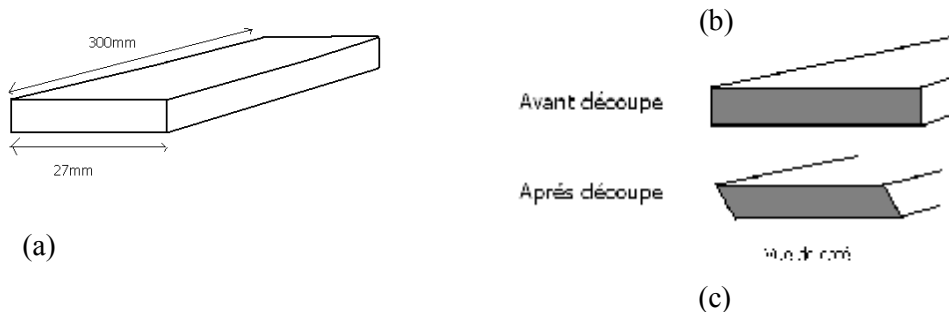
Découpe des plaques en PE : (a) dimensions des plaques, (b) plaque avant découpe et (c) plaque après découpe.
